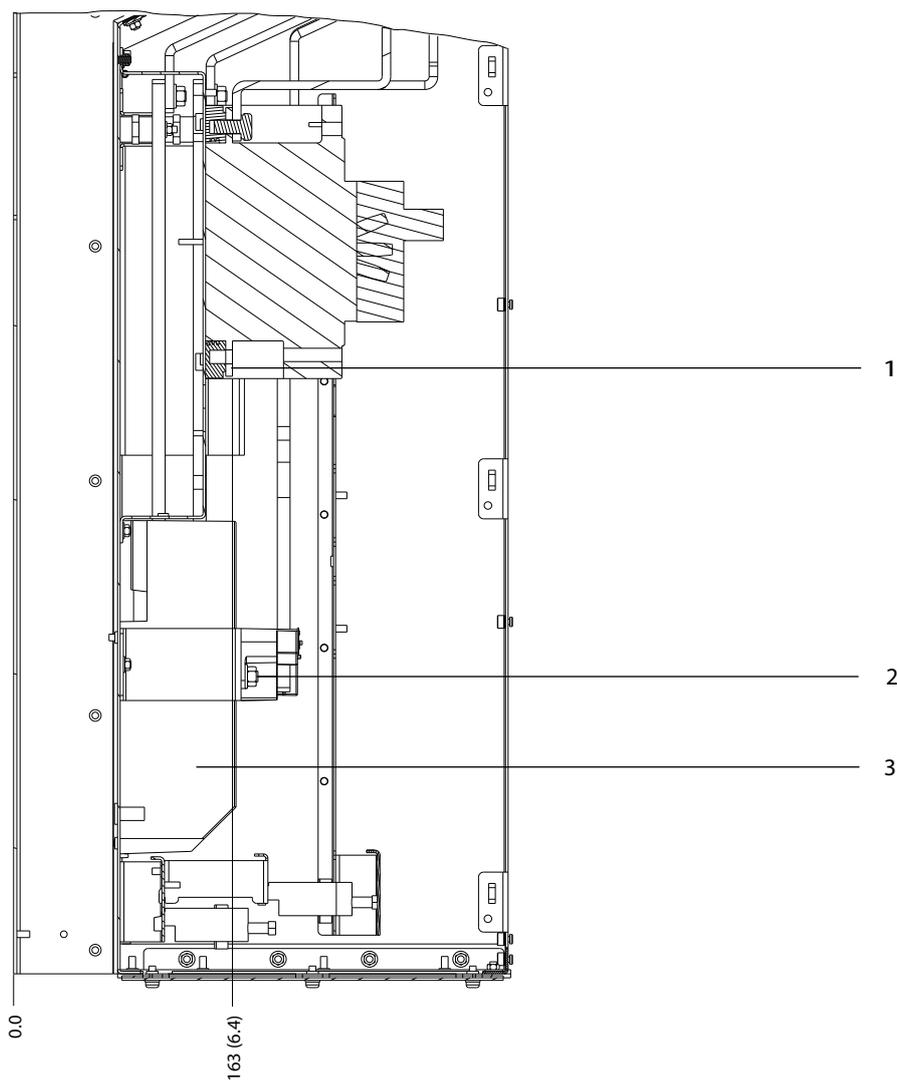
Dimensions des bornes D6h avec options contacteur et sectionneur (vues latérales)
